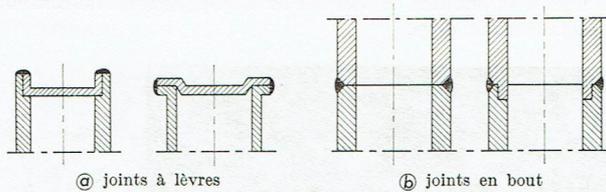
Formes de joints pour soudure argon-arc ou par bombardement électronique.
